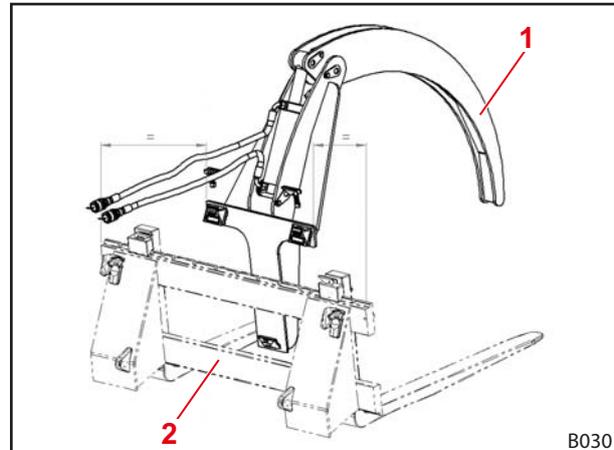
Werkzeug an Palettengabelrahmen anbauen
